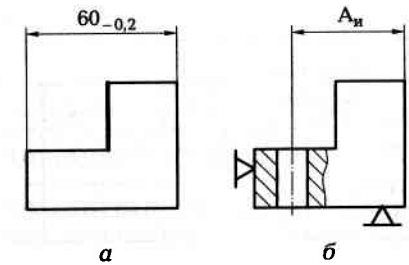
Схема базирования заготовки (а) при обработке (б) отверстия
